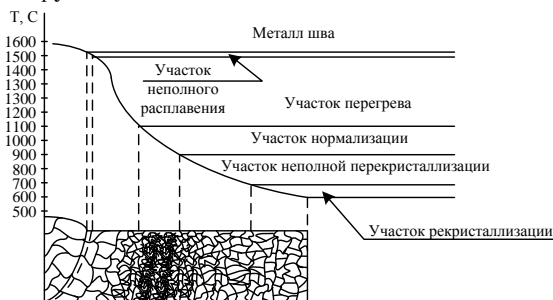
Схема строения ЗТВ сварного соединения
